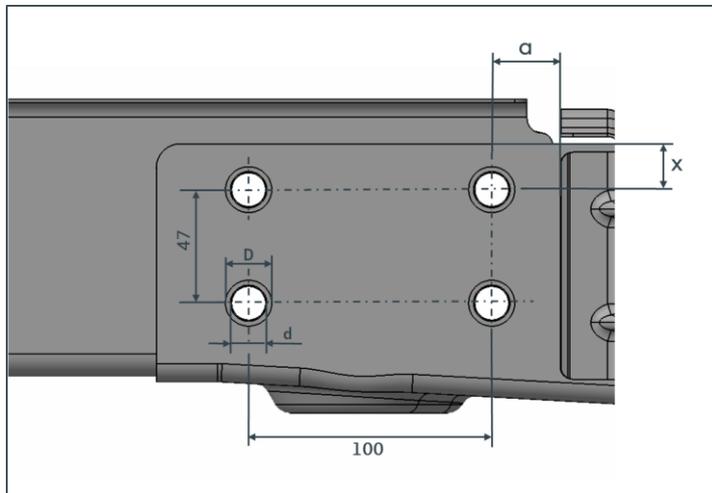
Fourgon 3,0 – 4,0 t (plancher bas)
